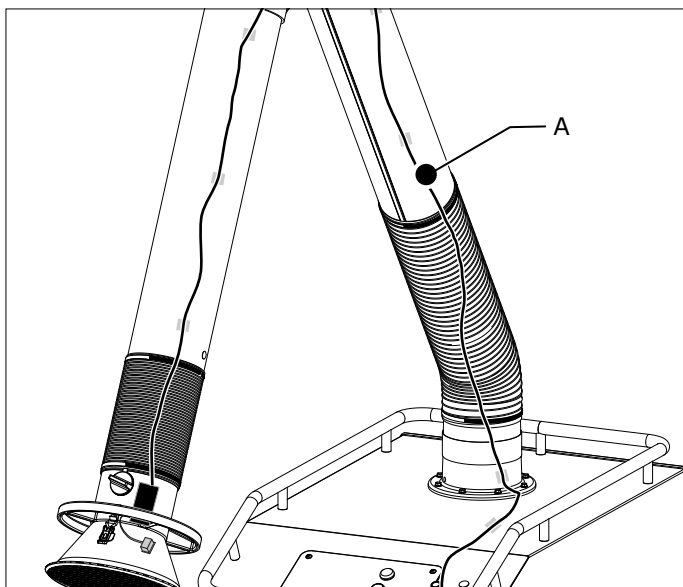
Montaje del cable de la lámpara de trabajo
